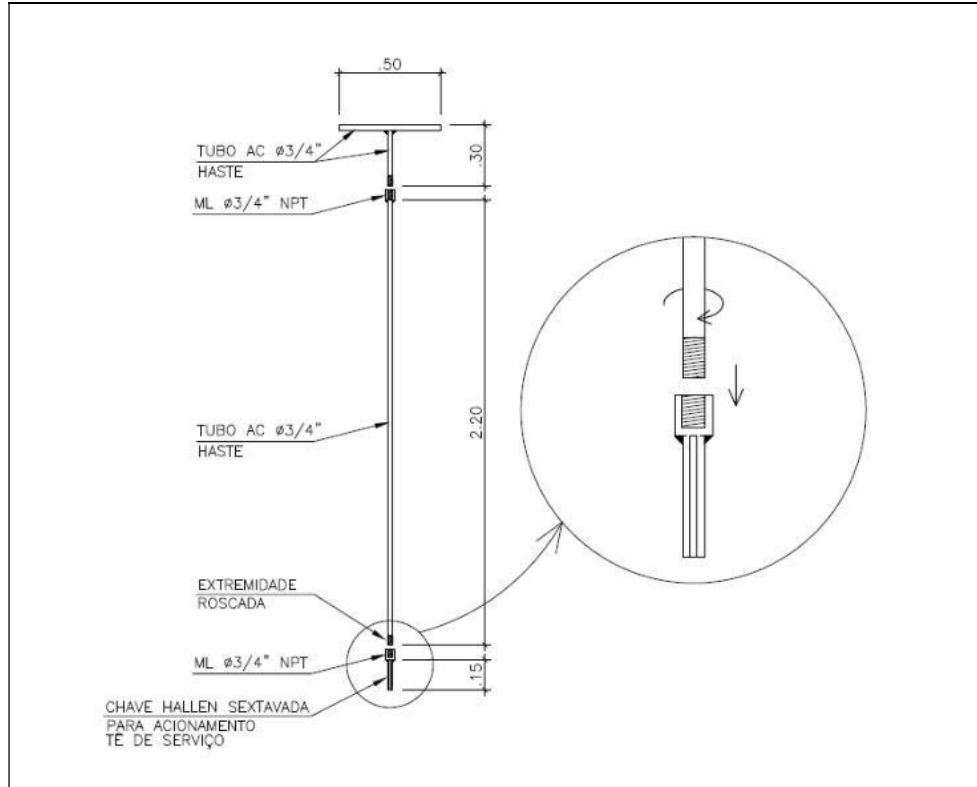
Dispositivo prolongador para furo de Te de Serviço
